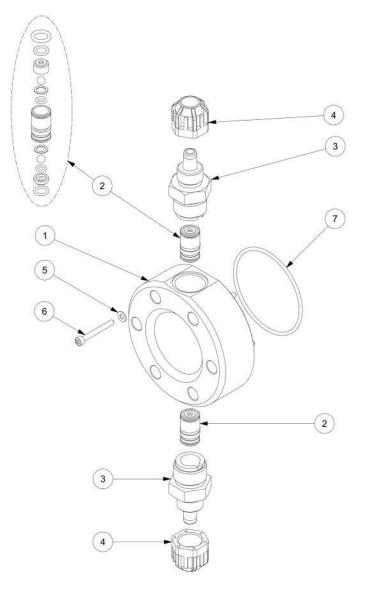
HC999 - Corpo pompa valvole a labbro e sfera / Pump head lip and ball valves / Corps pompe et clapets à lèvres et bille / Cuerpo de la bomba valvulas a labio y a esfera / Pumpenkörper Lippen- und Kugelventile / Головка насоса, губчатый и шариковый клапан
